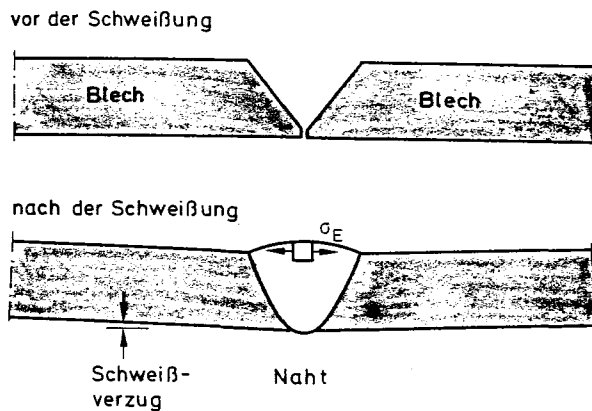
Schweißbeigenspannungen und Verzug
